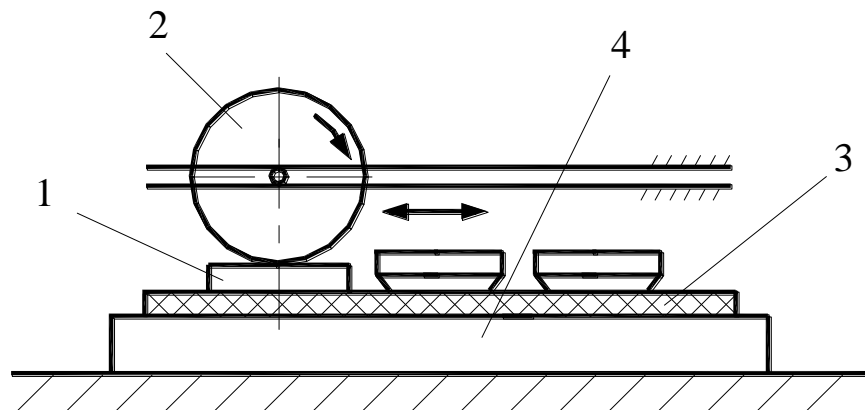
Схема установки для каткового способу розкроювання матеріалів
